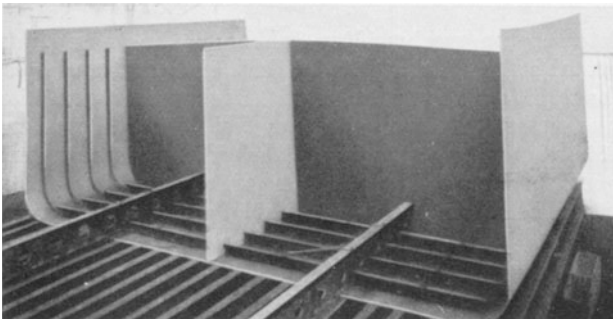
Teil eines ganz geschweißten Motortankboots.
